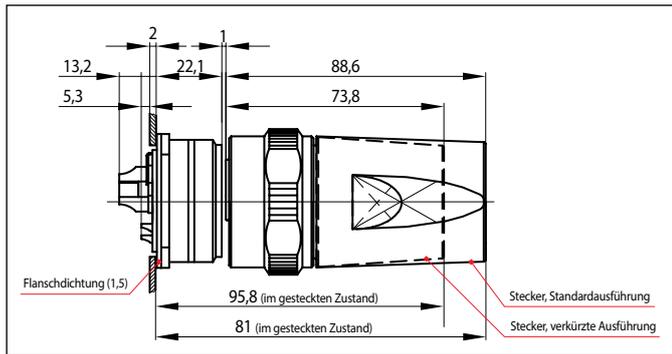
Einbaumaße und Maße im gesteckten Zustand für die Kombination Dose mit Flansch und Kabelstecker in Standardausführung sowie Dose mit Flansch und Kabelstecker in verkürzter Ausführung
